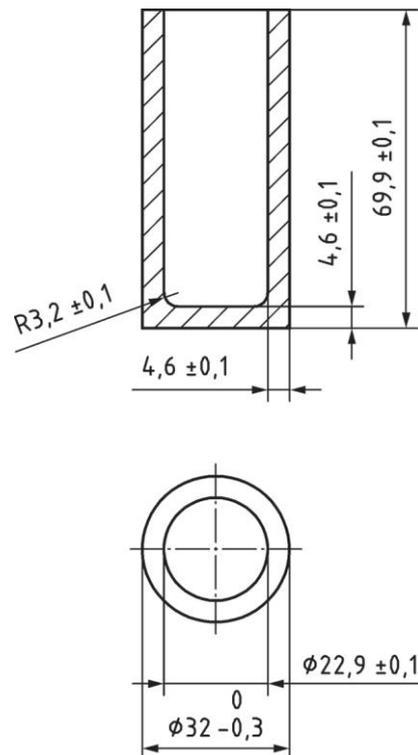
Чертеж и размеры цилиндрической полый втулки
